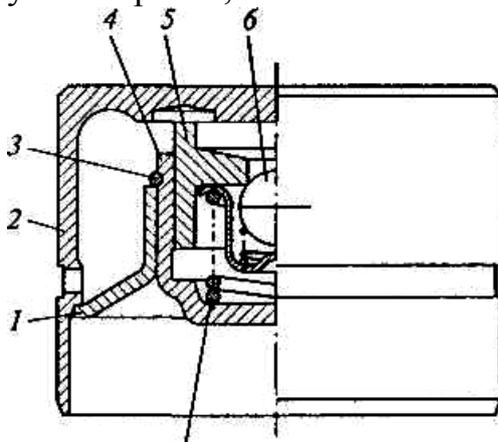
Гидравлический толкатель: 1 — втулка; 2, 4 — корпуса; 3 — кольцо; 5 — поршень; 6 — клапан; 7 — пружина
